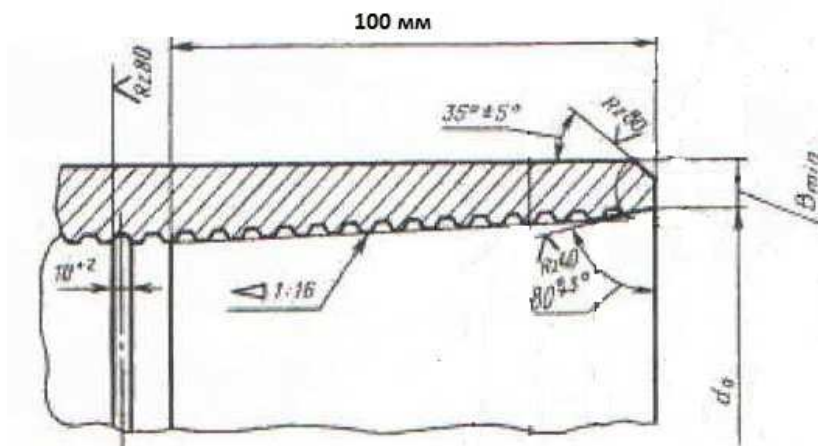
Вид резьбовой поверхностямуфты [3]
